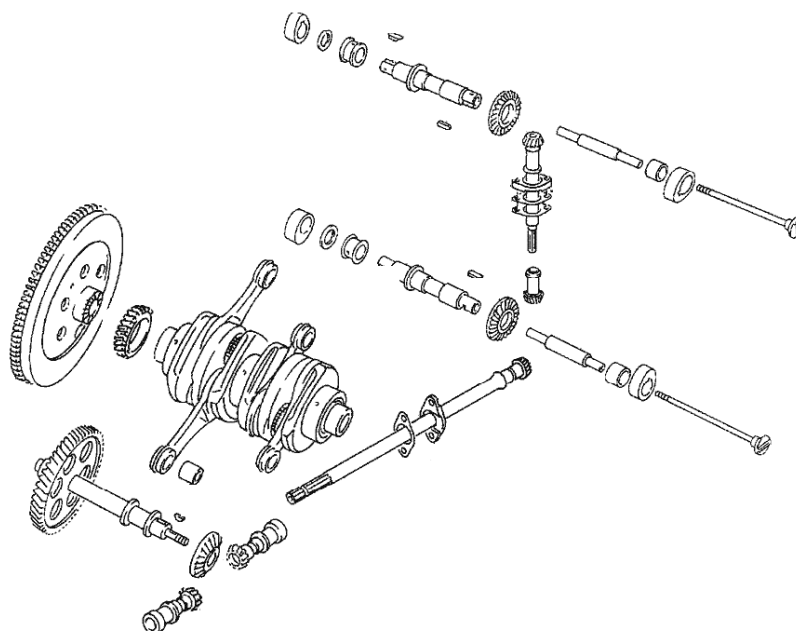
Motor Honda Gold Wing 1800 [19]
